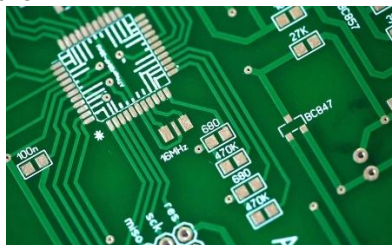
lapisan solder flux dan solder mask (sumber: <https://www.pcbaaa.com/pcb-solder-mask/>)
